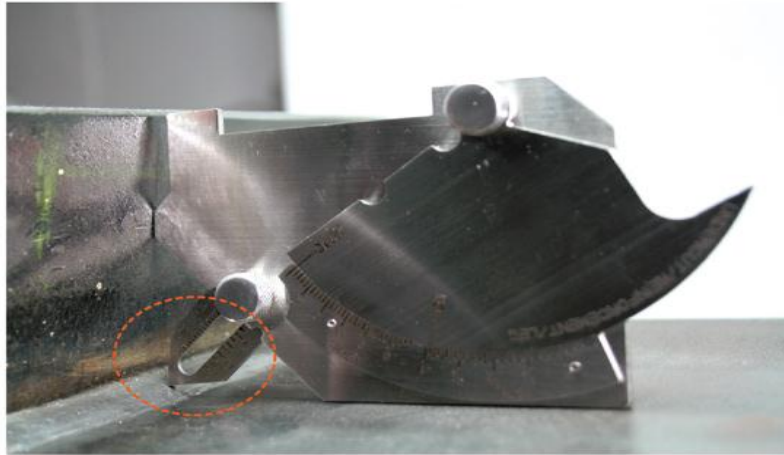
Tamaño de la garganta de soldadura de filete
